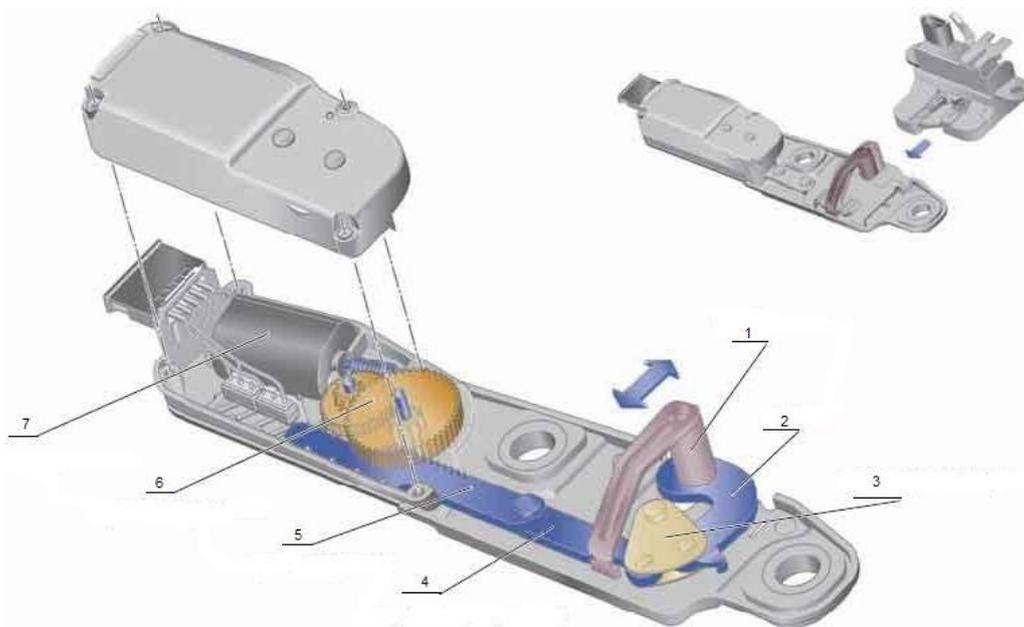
конструкция электропривода: 1 - скоба замка; 2 - рычаг; 3 - промежуточный рычаг; 4 - промежуточная рейка; 5 - зубчатая рейка; 6 - зубчатая передача; 7 - электродвигатель
